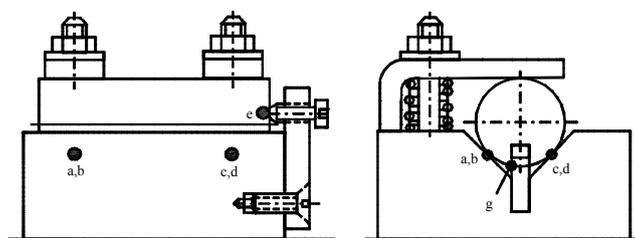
Схема установки заготовки вала с использованием призмы
